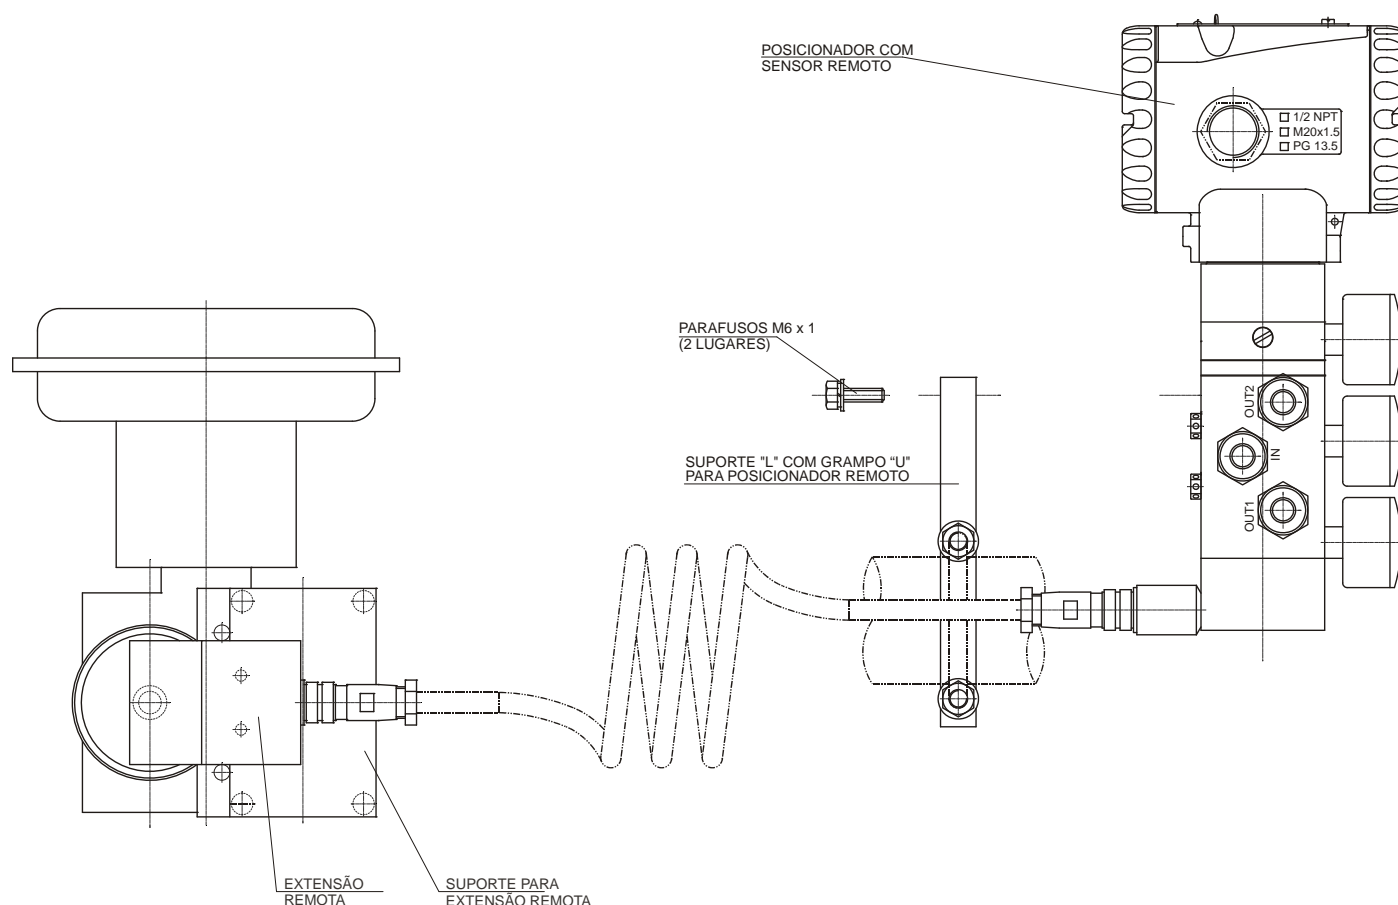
Posicionador em Atuador Rotativo com Sensor de Posição Remoto
